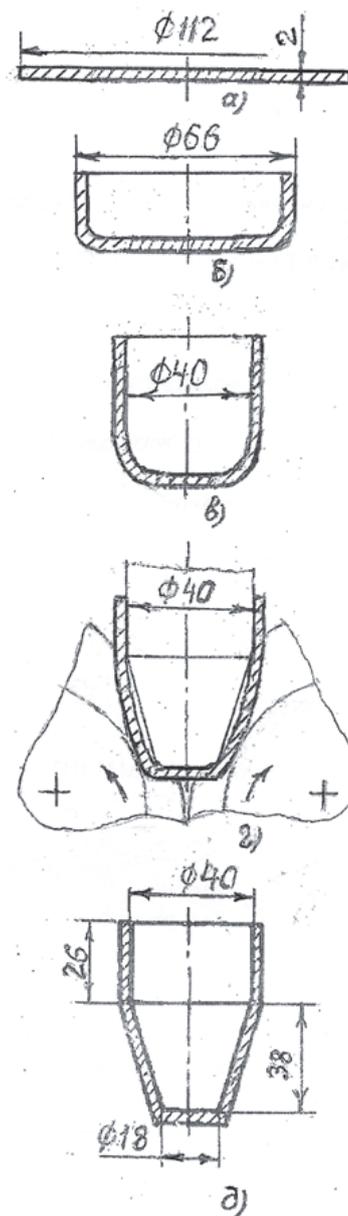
Последовательность формоизменяющих переходов вытяжки из круглой заготовки детали с конической придонной частью
